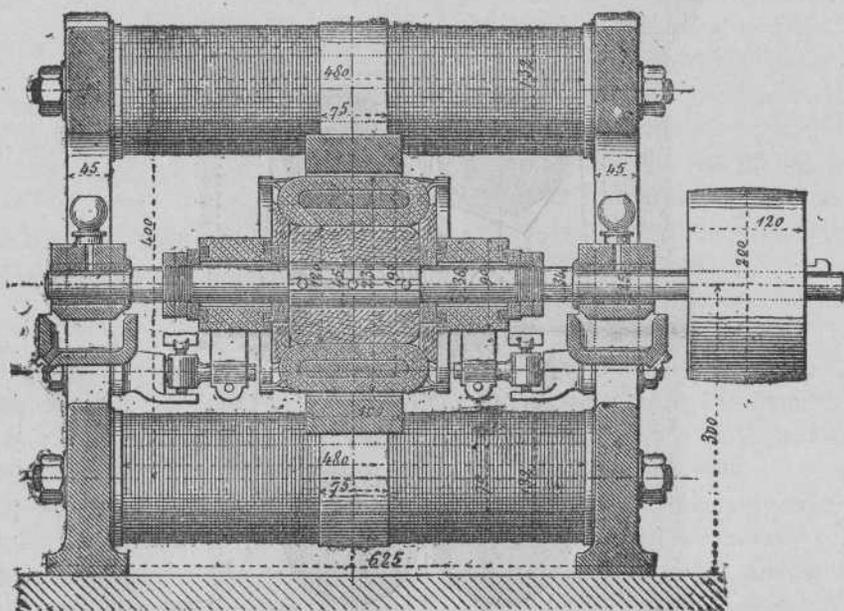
Máquina Gramme de cuatro electro-ímanes horizontales. Corte longitudinal.
